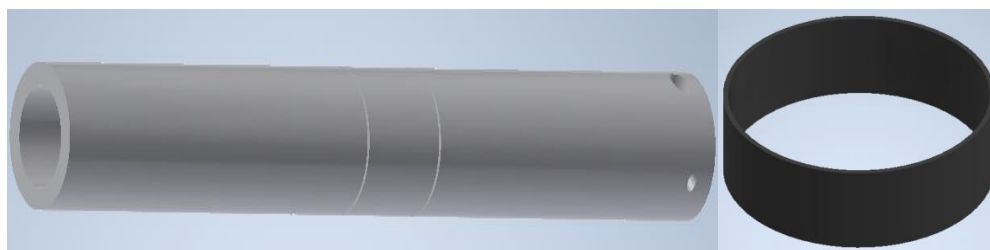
3Д модель металлической трубы и прокладки для крепления колеса
